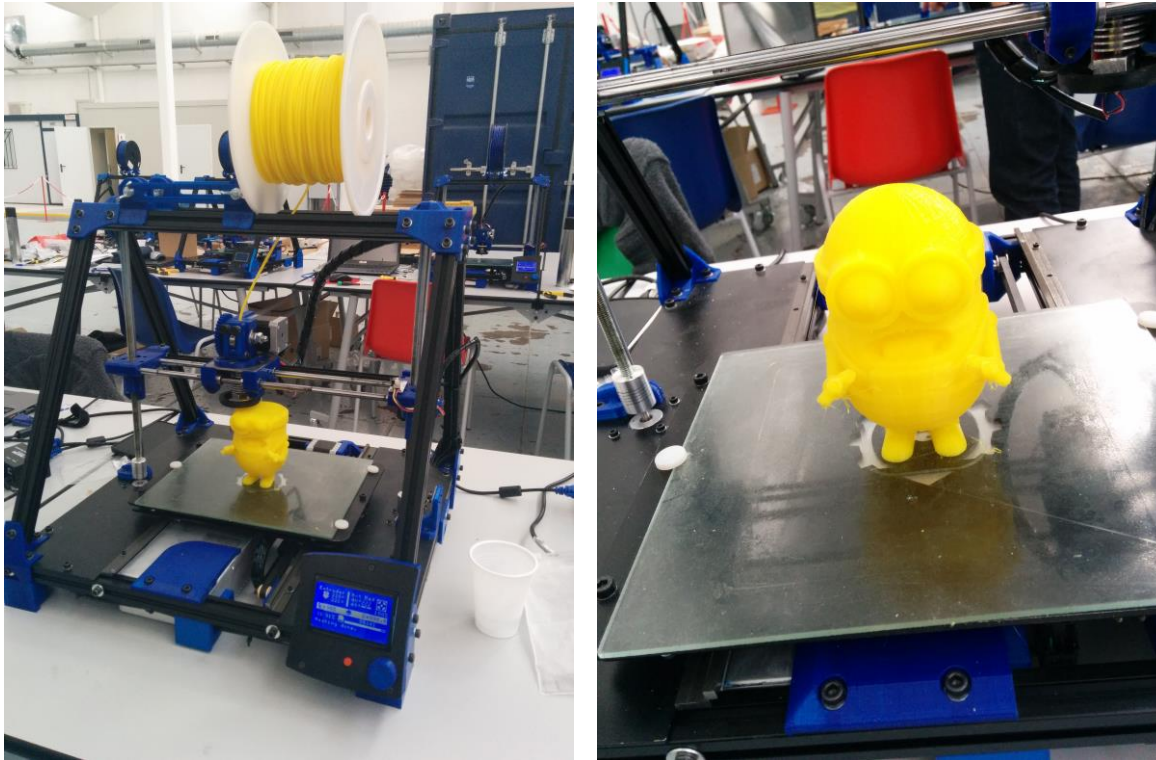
Izquierda: Proceso de impresión con la RepRapBCN3D+. Derecha: Resultado de la impresión 3D
